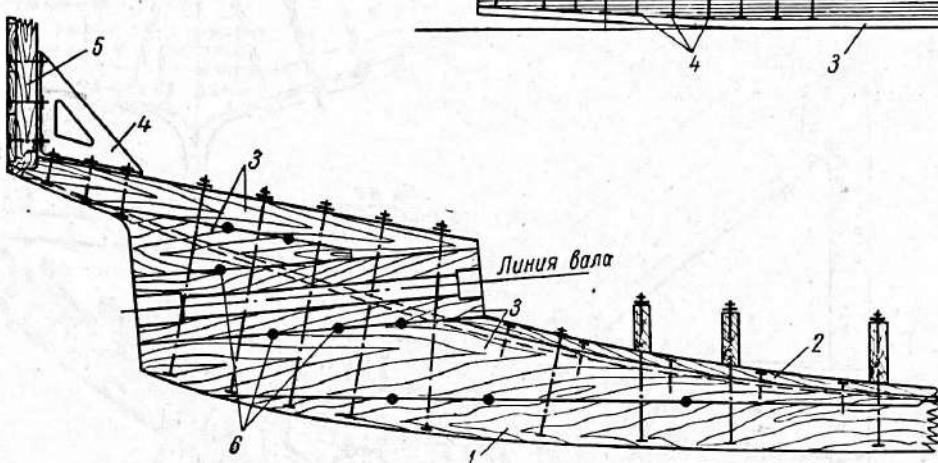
Набор кормового дейдвуда для катера (болтовое крепление).
